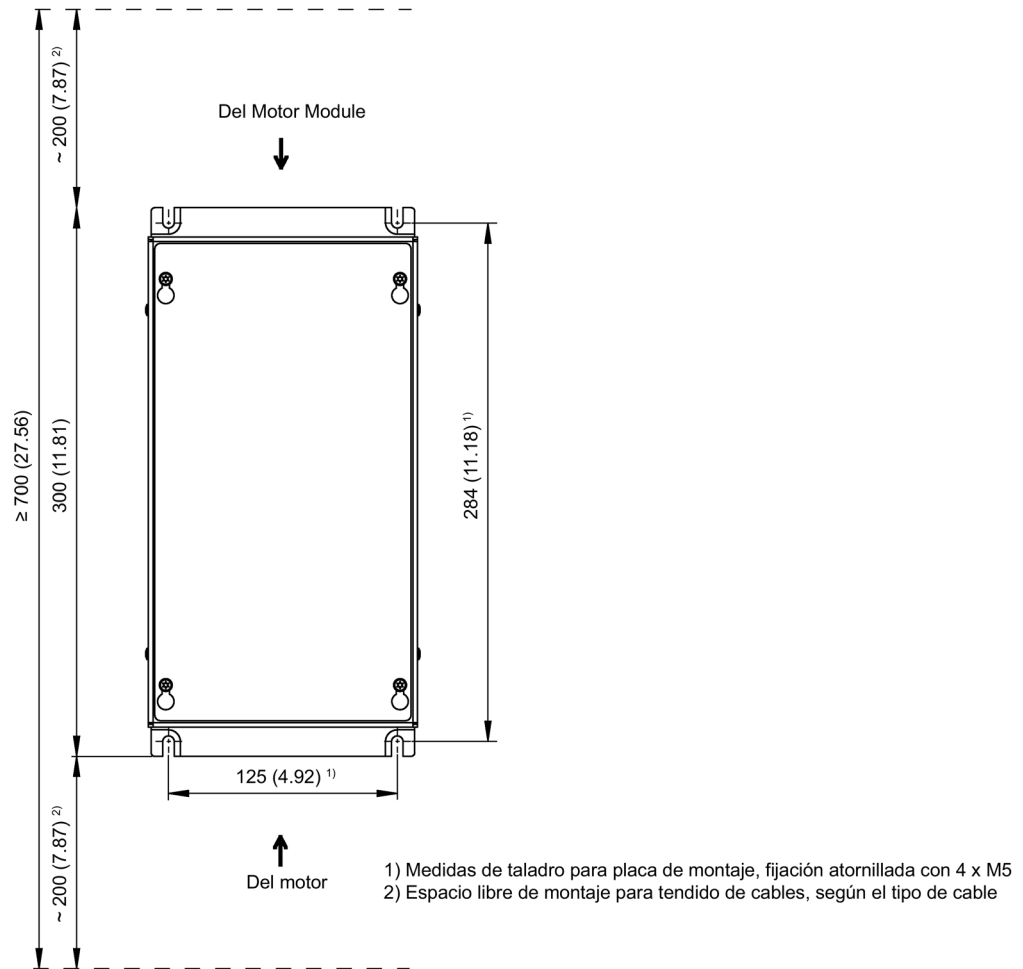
Dimensiones de montaje de un Voltage Protection Module VPM120
